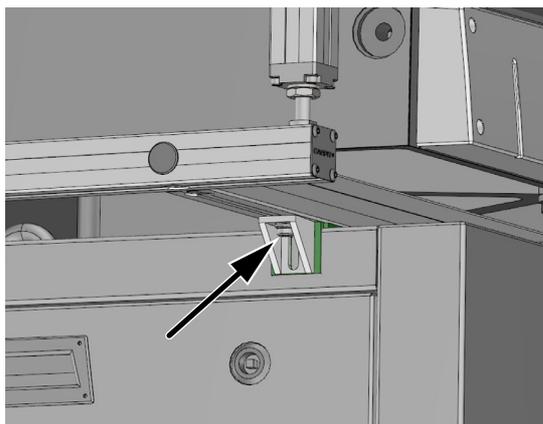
Winkel anschrauben Profil (Abbildung beispielhaft)
